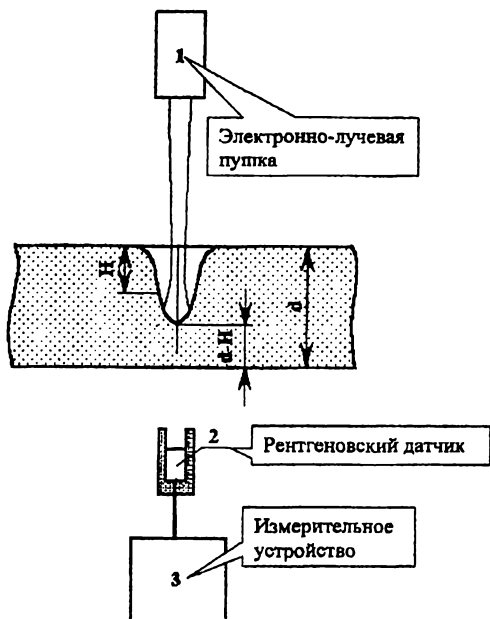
Схема контроля глубины проплавления рентгеновским датчиком, размещенным с обратной стороны сварного шва
